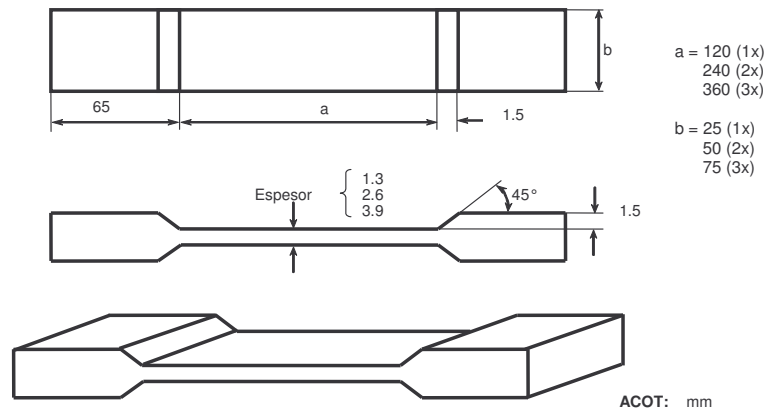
Geometría y dimensiones de las probetas para la prueba de tensión.
